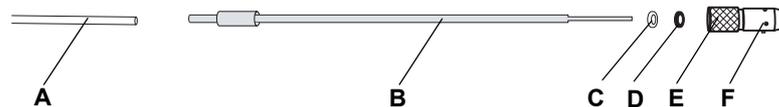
Embouts Te-PS, vue d'ensemble
